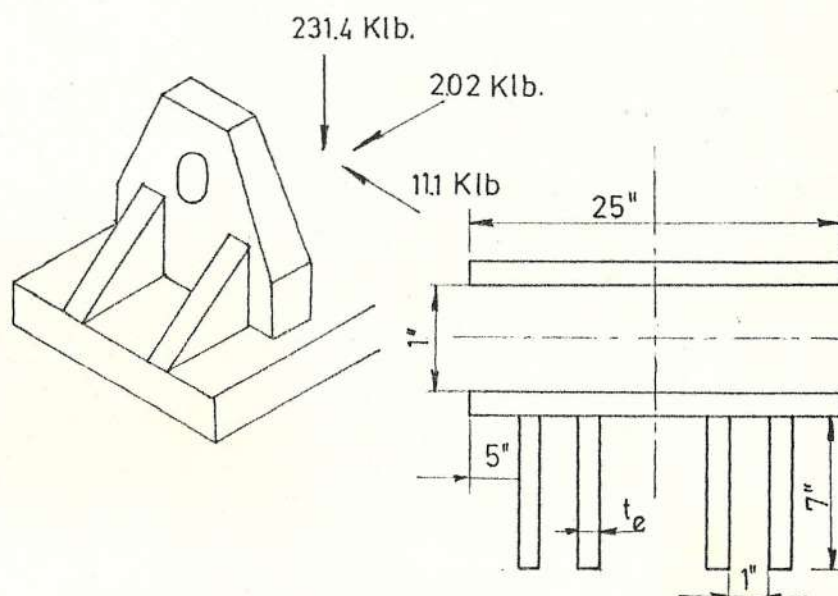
DISEÑO DE LA SOLDADURA PARA EL APOYO EXTERIOR.
